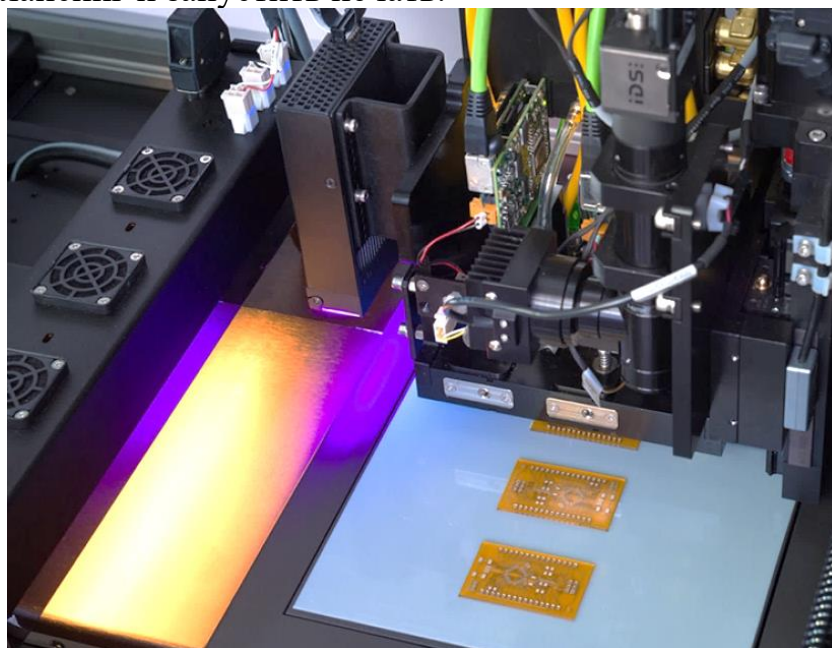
Рабочая платформа Nano Dimension DragonFly 2020 Pro
